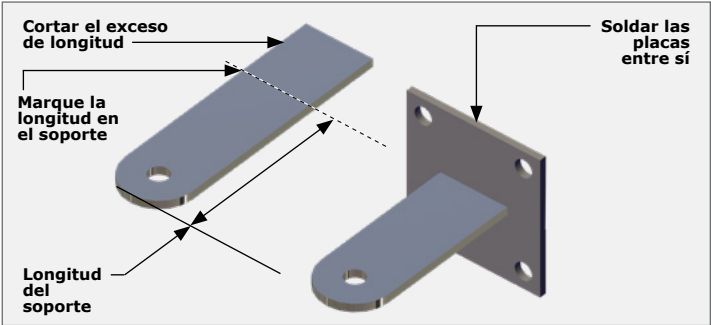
CORTAR Y SOLDAR EL SOPORTE DE PARED
